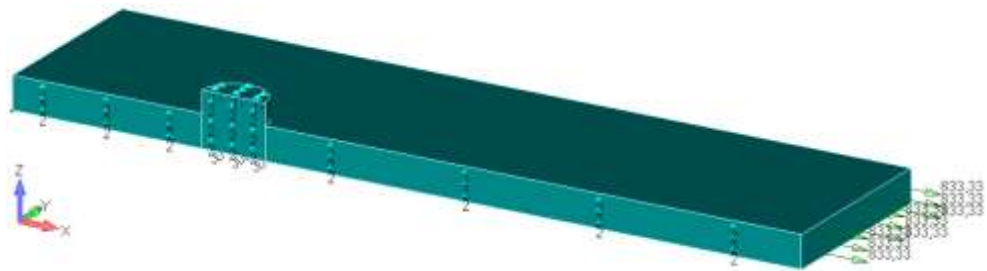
Розрахункова модель пластини у контакті з циліндром ("болтом")
